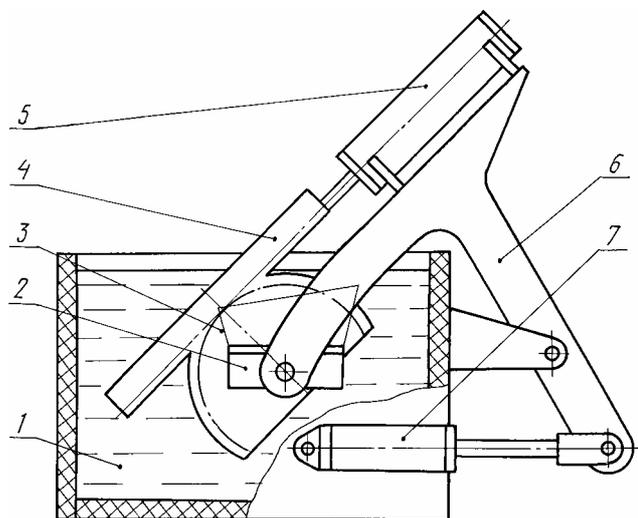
Стенд для контроля герметичности головки цилиндров: 1 – ванна; 2 – плита; 3 – сектор зубчатый; 4 – рейка; 5 и 7 – пневмоцилиндры; 6 – рычаг
